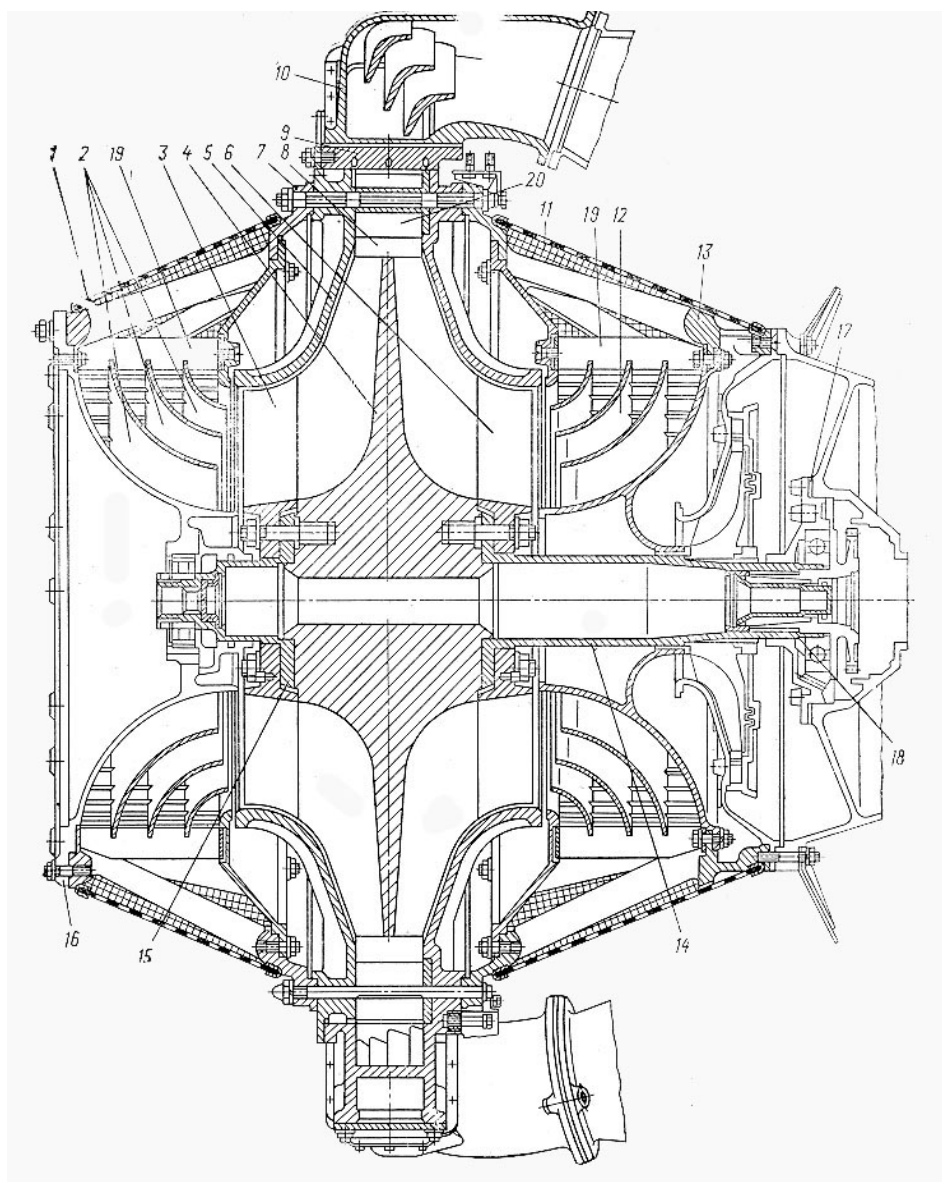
Продольный разрез центробежного компрессора с двухсторонним входом:
